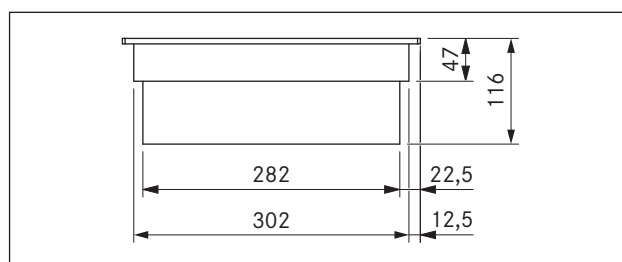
Dimensões do aparelho CKIW, vista frontal
